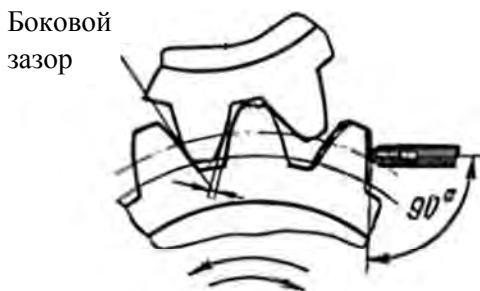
Схема измерения бокового зазора между зубьями зубчатых колес с помощью индикатора
